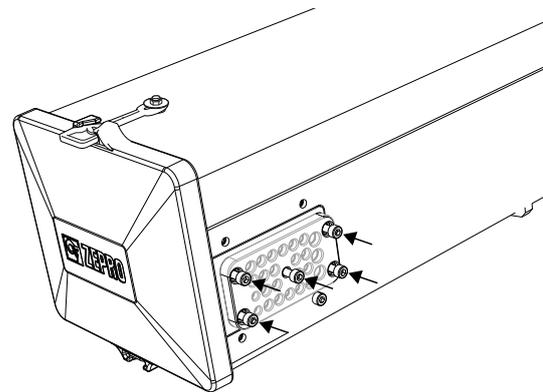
Die fünf Schrauben der Kabeldurchführung
